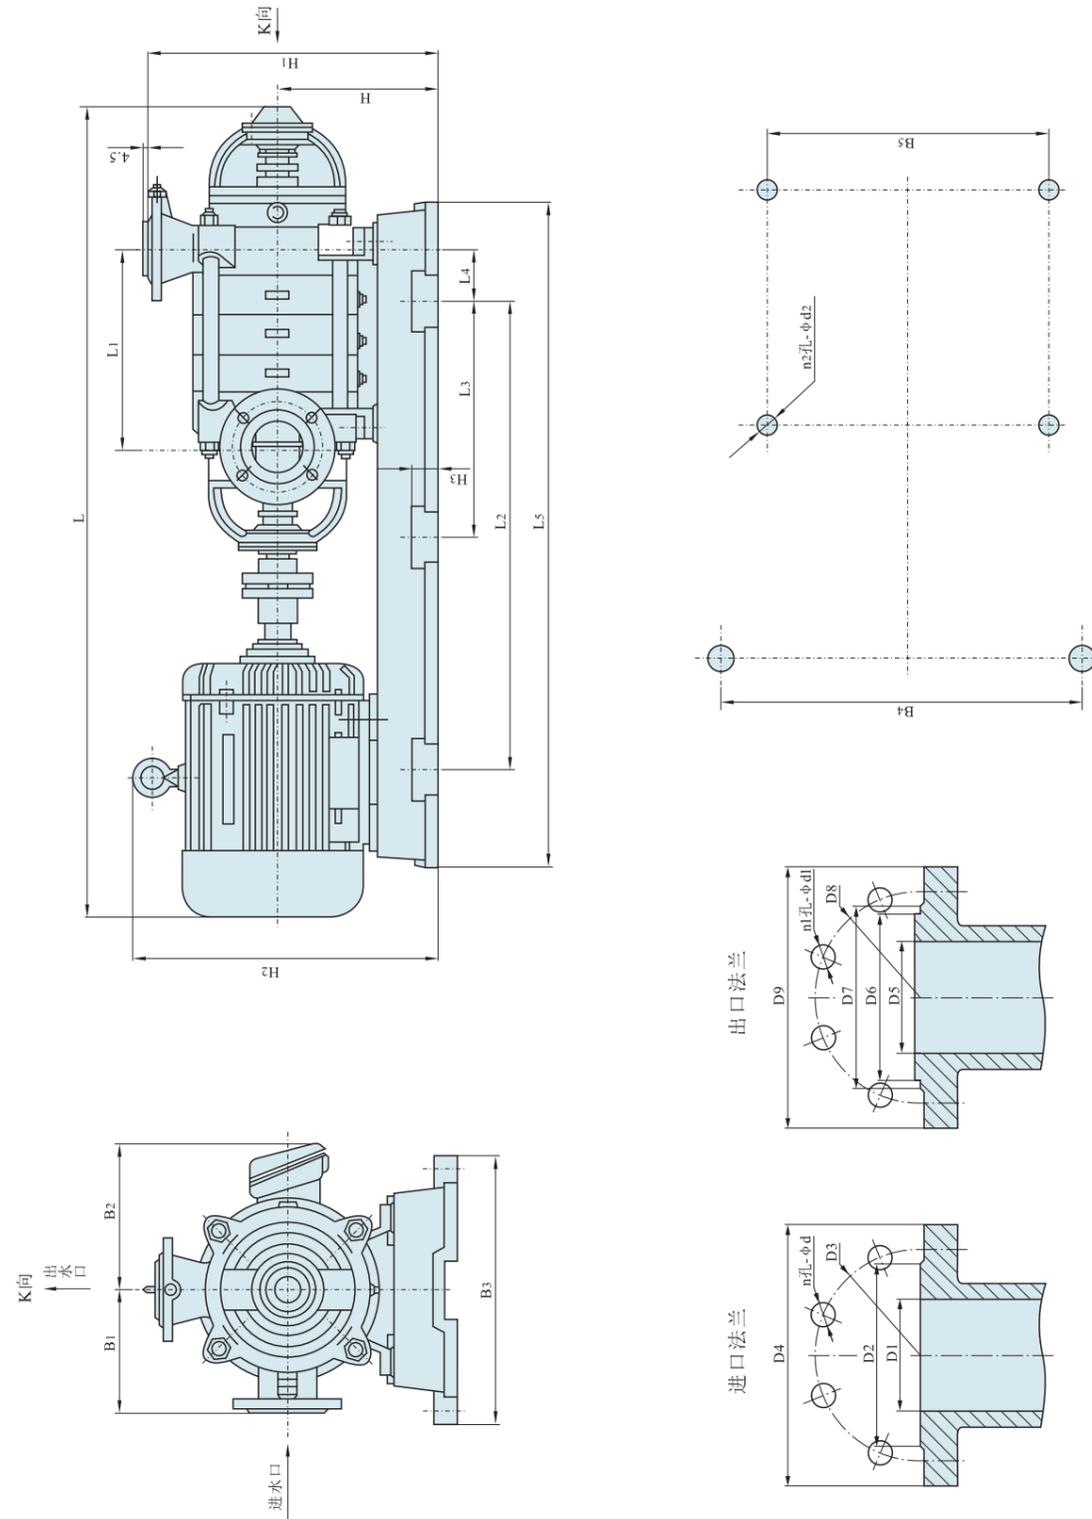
65SLD25-30、80SLD46-30型泵的外形及安装尺寸图 Fig.3 Figure and dimension figure for series pump
